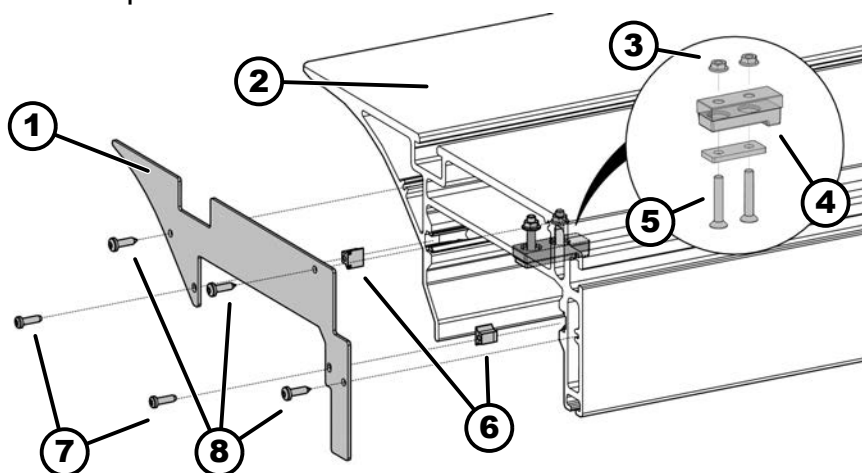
Cubierta del carro deslizante y mordazas de tope
